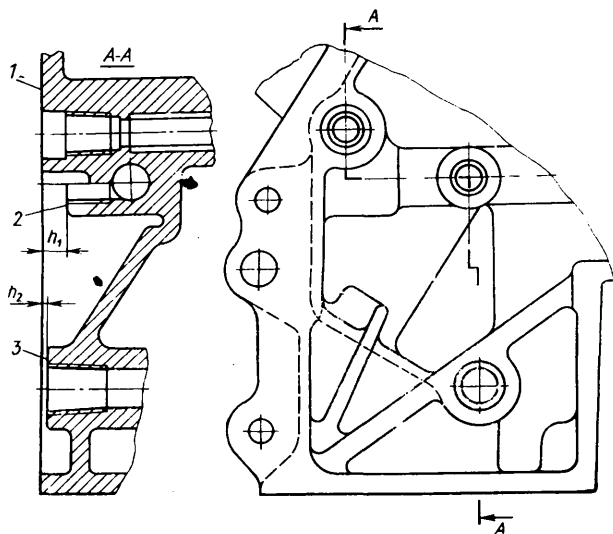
Вид на задний торец блока цилиндров двигателя автомобиля ГАЗ-66
